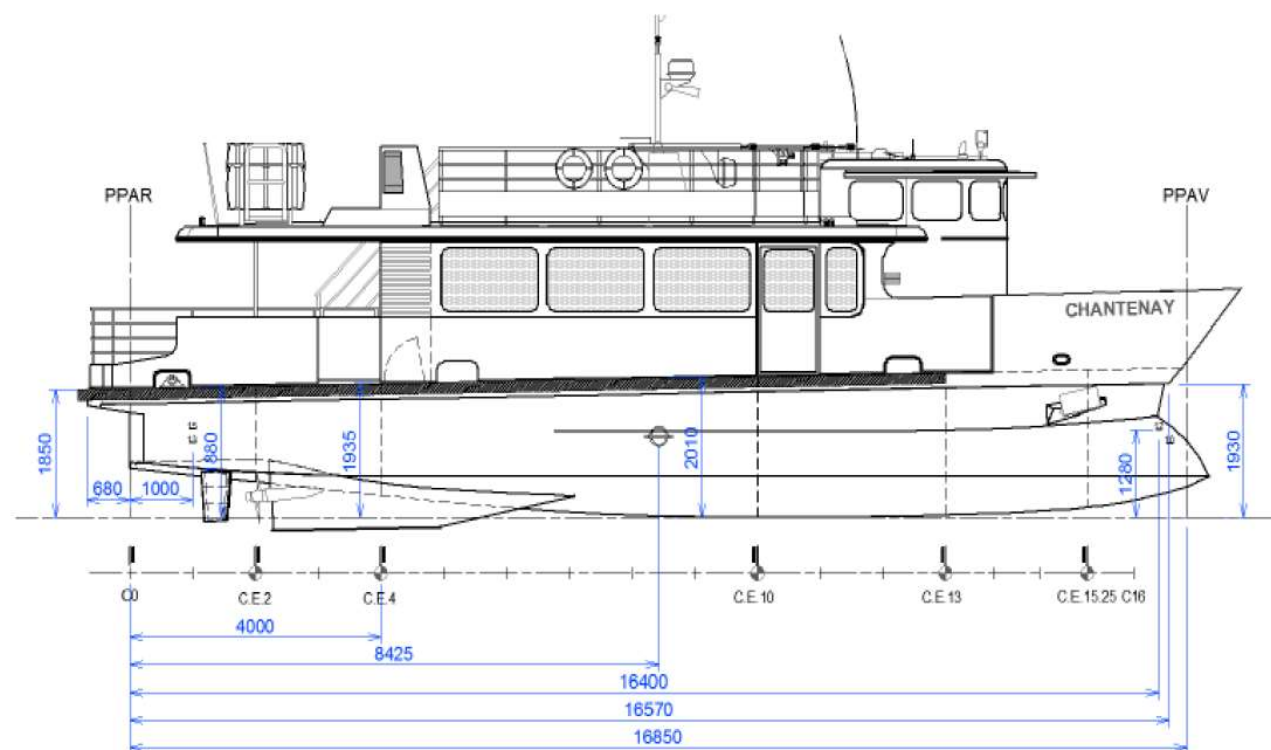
Plan d'un navire type (SCE, décembre 2023)
